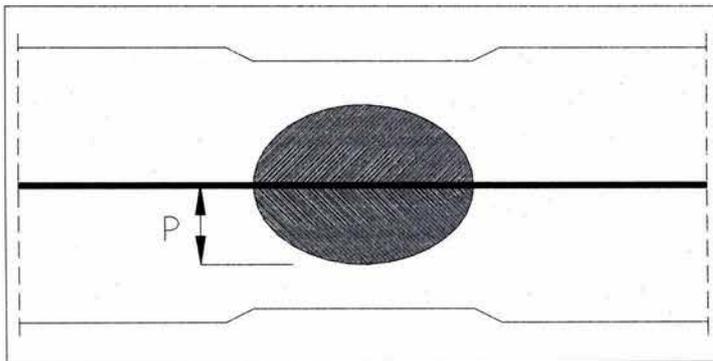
Especificaciones mínimas para evaluar la dimensión de un punto de soldadura.
